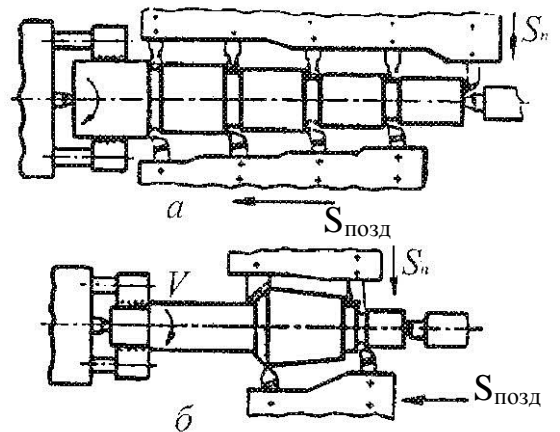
Схеми обробки заготовок на токарному багаторізцевому напівавтоматі
